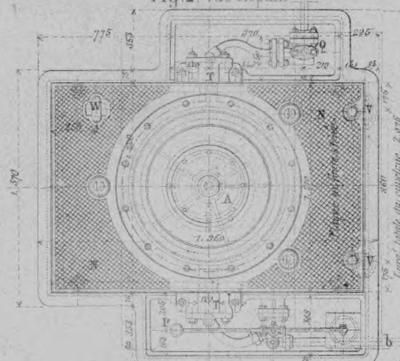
Vue en plan, le cabestan retourné (Plan view, the turned-around block winch)
